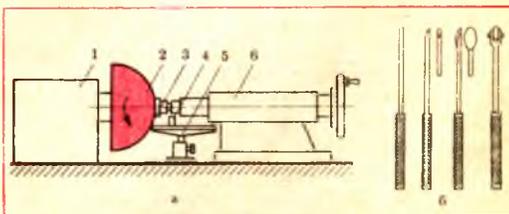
Устройство для давильных работ (а) и давильники (б): 1 — токарный станок; 2 — выдавленная заготовка на оправке; 3 — прижим; 4 — опорный штифт; 5 — упор; 6 — задняя бачка
